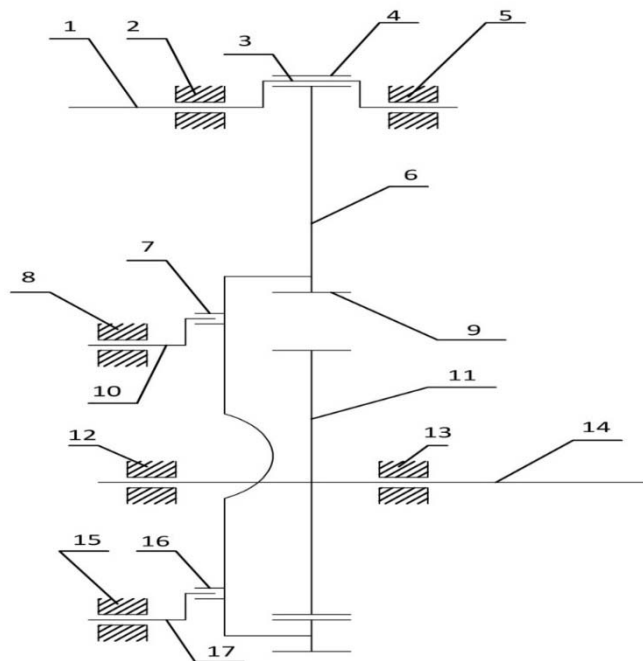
Структурная схема эксцентриковой передачи с параллельным расположением входного и выходного валов: 1 – входной вал; 2 – подшипниковая опора; 3 – кривошип; 4 – опорная втулка; 5 – подшипниковая опора; 6 – сателлит; 7 – опорная втулка; 8 – подшипниковая опора; 9 – внутренний зубчатый венец; 10 – кривошип; 11 – центральное колесо; 12 – подшипниковая опора; 13 – подшипниковая опора; 14 – выходной вал; 15 – подшипниковая опора; 16 – опорная втулка; 17 – кривошип
